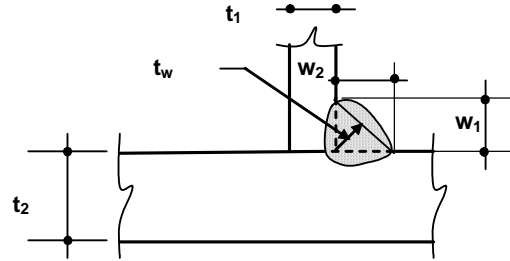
Soldadura de filete. Junta en Te.
